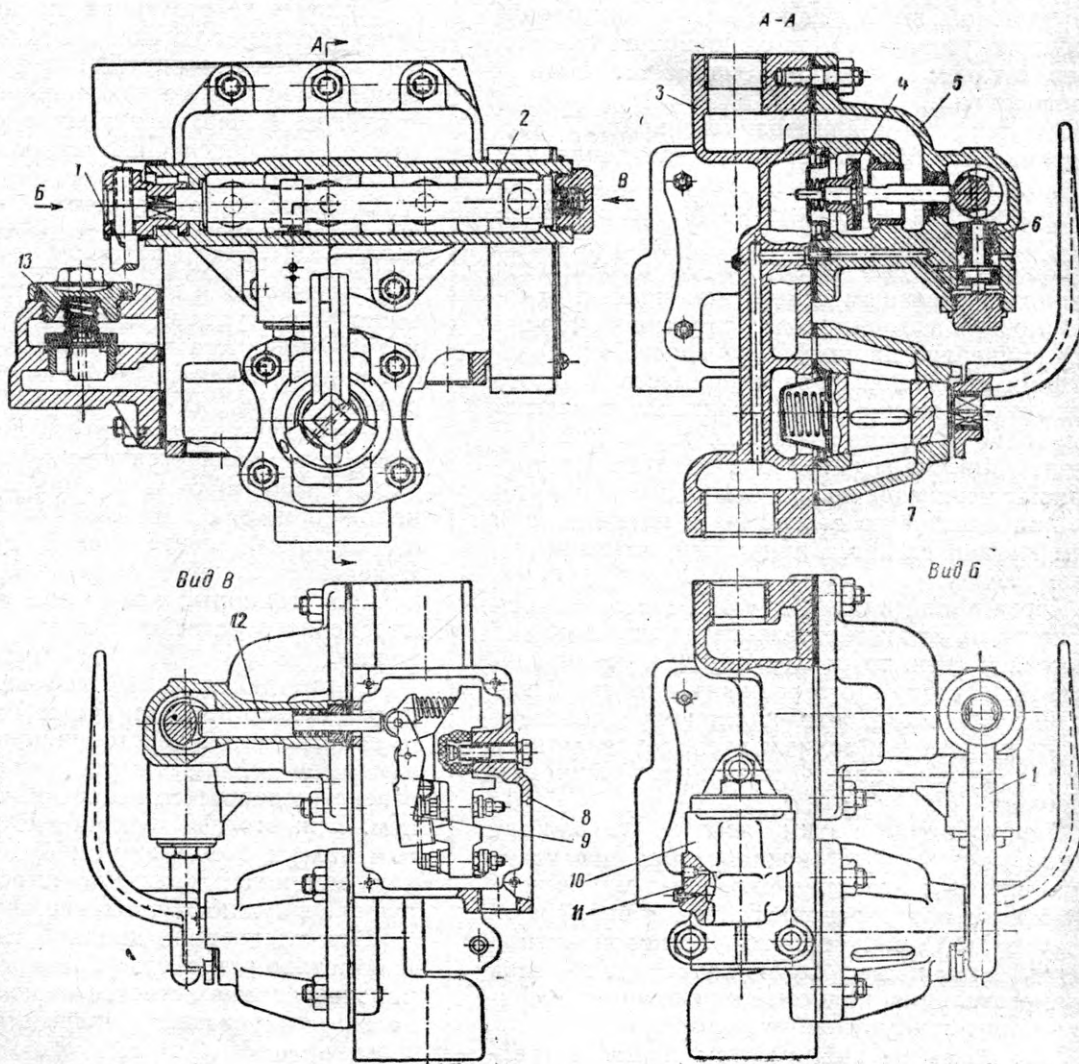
Общий вид устройства блокировки тормозов усл. № 367:
